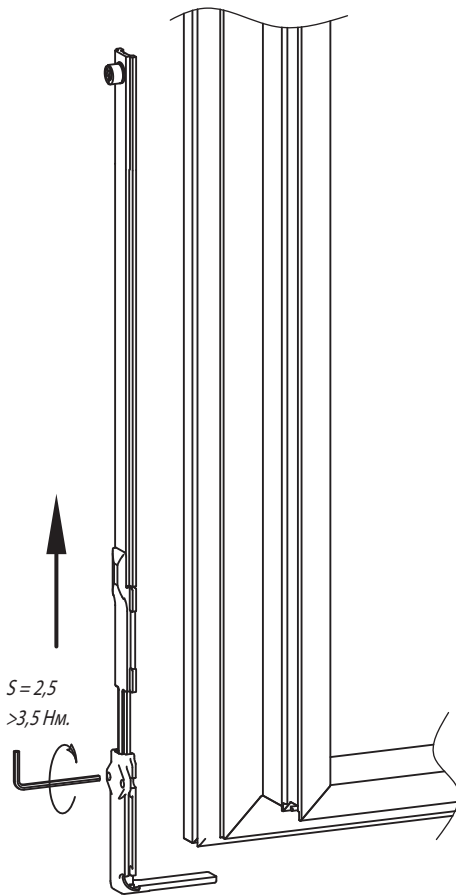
Установка узлов со стороны левой боковой стойки
